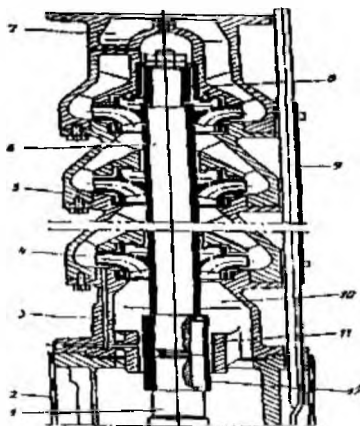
Центробежный многоступенчатый скважинный погружной насос типа АП (агрегат погружной): 1 – вал электродвигателя; 2 – сетчатый фильтр; 3 – канал системы смазывания подшипника, 4 – рабочее колесо первой ступени; 5 – секция корпуса насоса; 6 – вал насоса; 7 – отвод; 8 – верхний подшипник; 9 – электрокабель; 10 – подвод первой ступени ротора; 11 – нижняя подшипниковая опора; 12 – жесткая соединительная муфта
